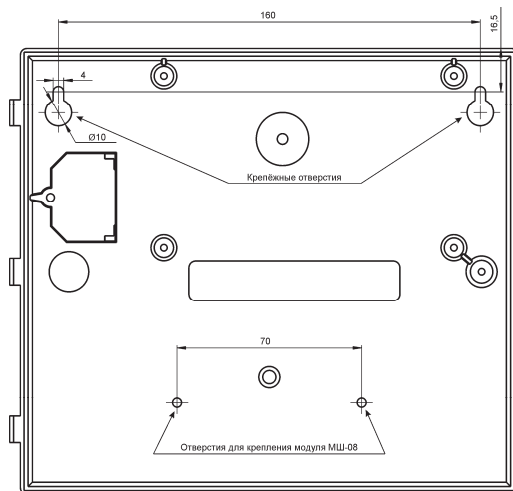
Установочный чертёж корпуса (вид изнутри)
